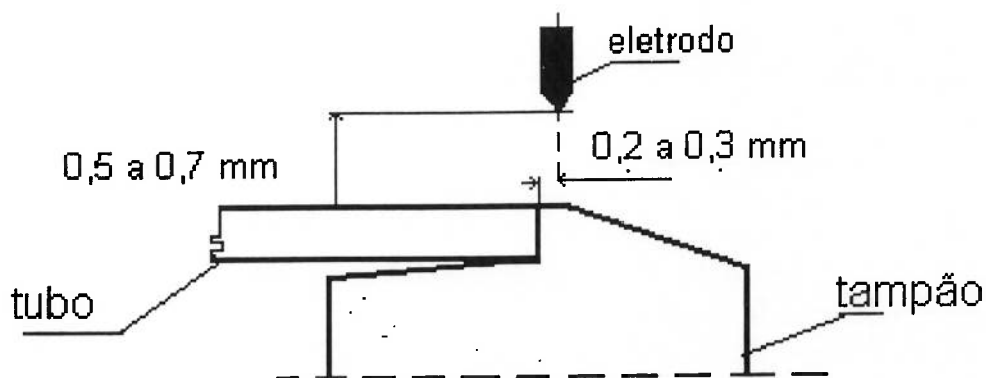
Posicionamento do eletrodo em relação às peças a serem soldada
